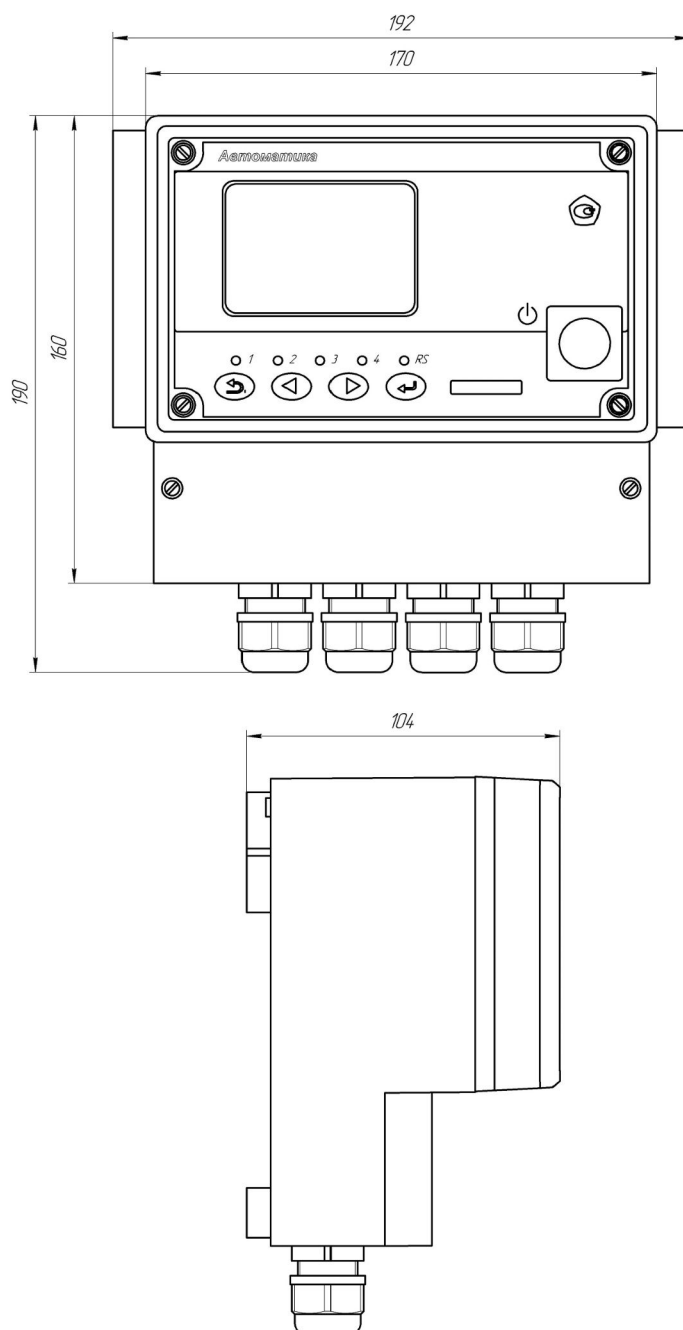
Габаритные размеры измерительного прибора АРК-5101
